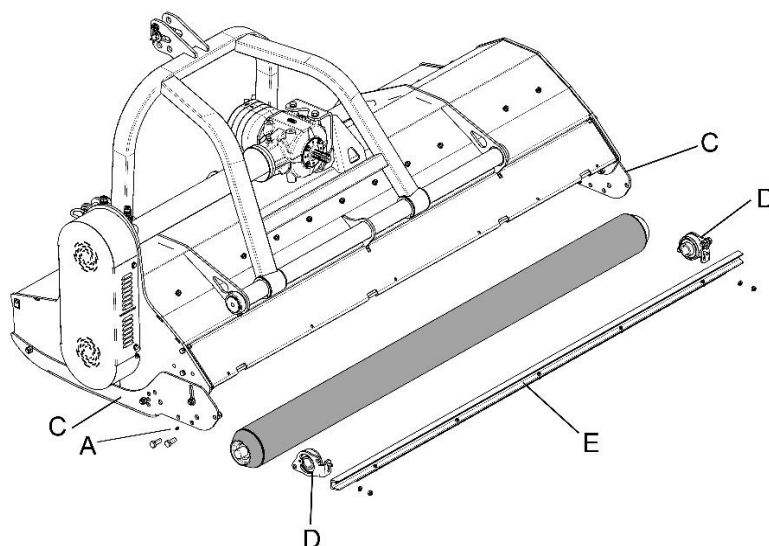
Pozycja zewnętrzna rolki wspierającej
